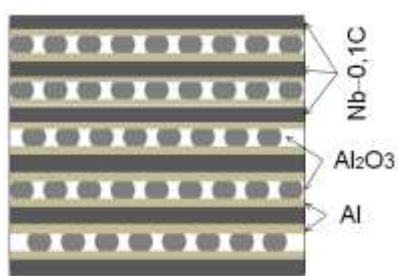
Схематическое изображение собранного пакета до диффузионной сварки
